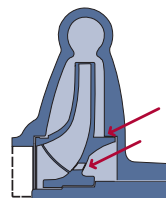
Баланс осевых сил в одноступенчатом центробежном насосе с уплотнительными зазорами в напорной части и разгрузочными отверстиями
